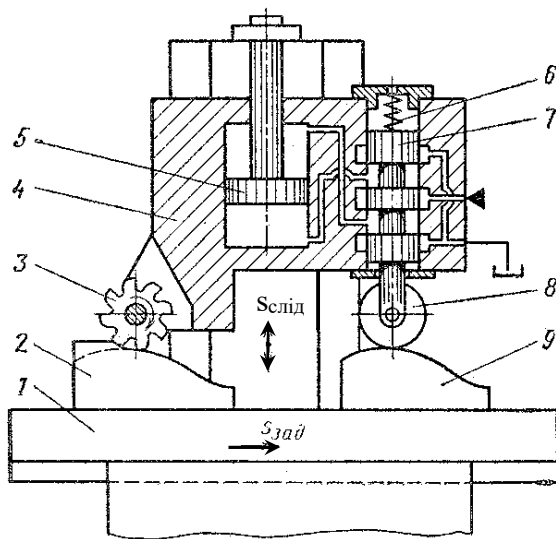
Схема гідравлічної копіювальної системи фрезерного верстата
